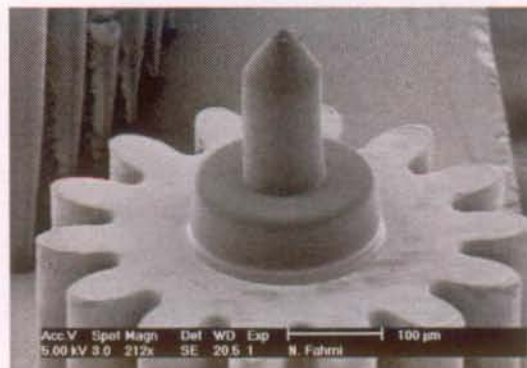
Positionnement d'une pointe sur un pignon en SU-8.
